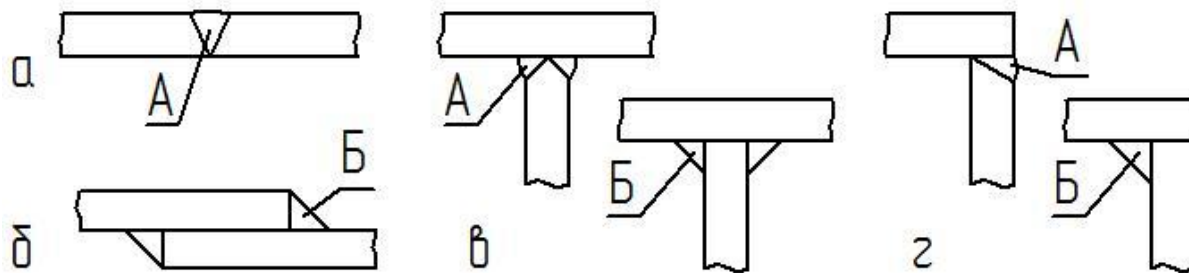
Види зварних з'єднань і типи зварних швів
